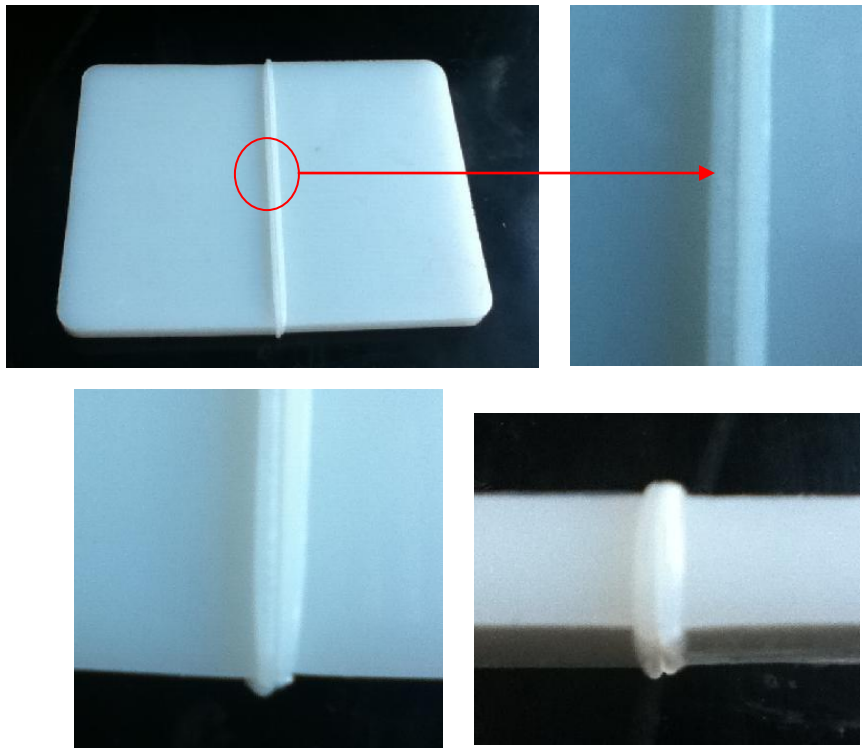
Cordón de soldadura de las placas de PE. En el centro es homogéneo, y a medida que se acerca a los bordes disminuye su espesor.
